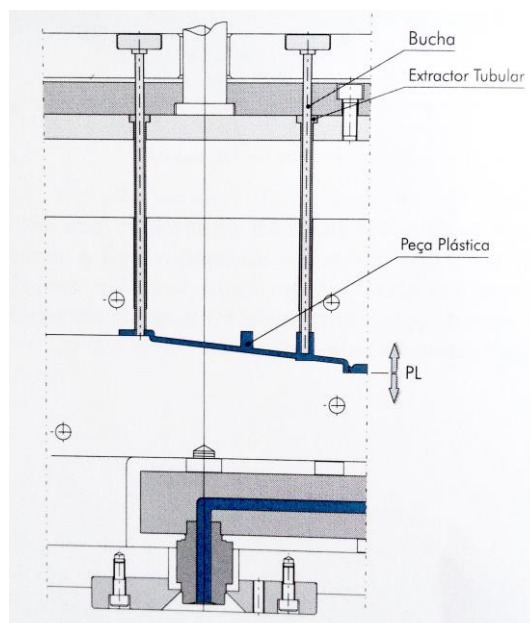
Vista em corte de um molde com extrator tubular [1].
